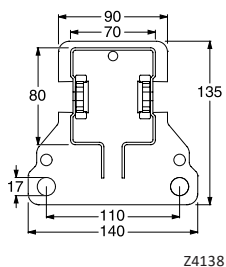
Průřezy sloupků opěrných profilů (všechny rozměry v mm)
